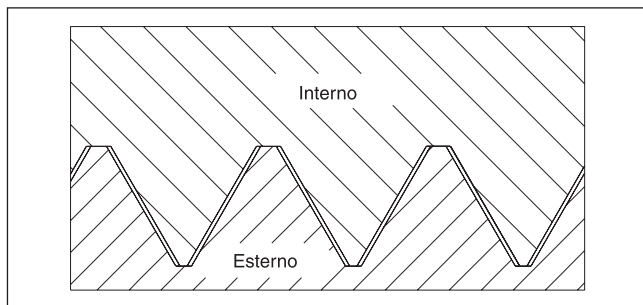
NPTF – Contatto cresta-fondo con serraggio a mano.
